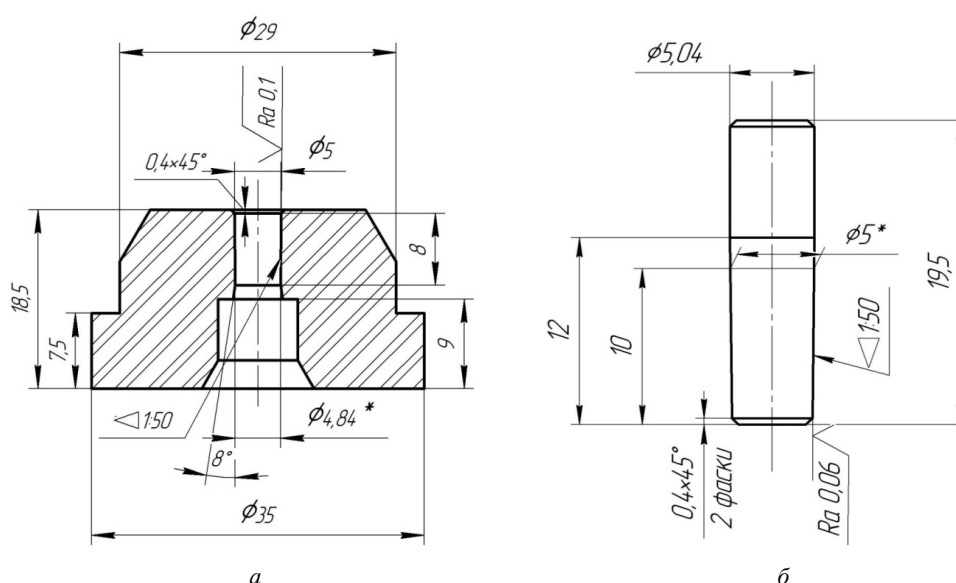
Эскизы охватывающей (а) и охватываемой (б) деталей
